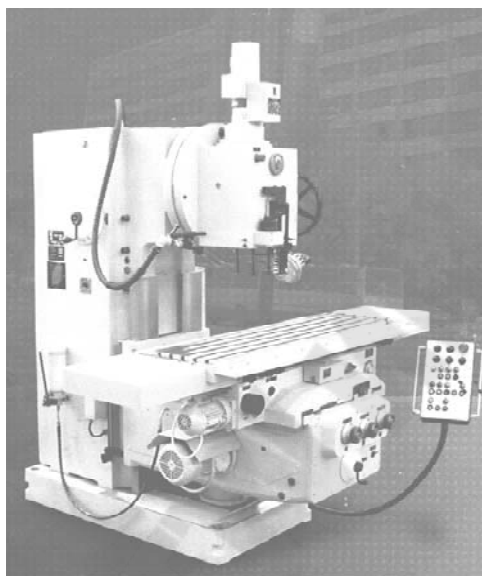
Общий вид консольно-фрезерного станка модели 6Р13Б
